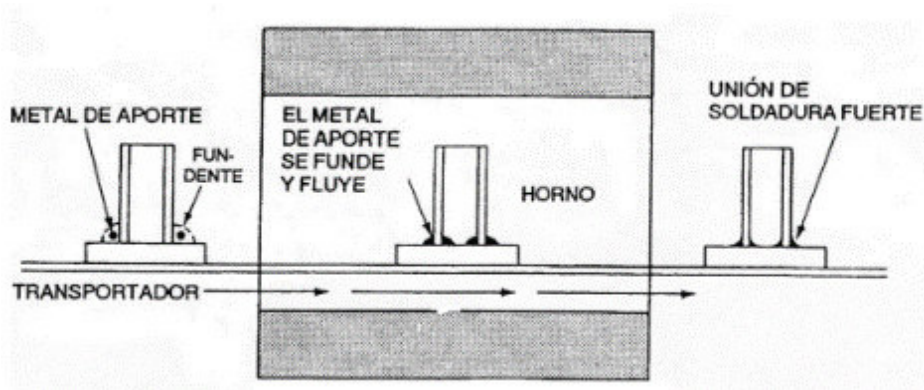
Descripción del proceso de soldadura fuerte por horno.
